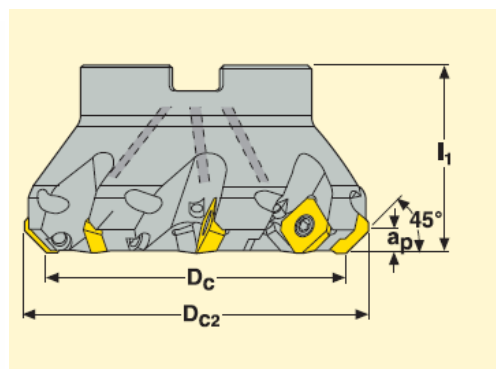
Фреза торцовая $\varnothing 20$ R217.53 – 0040-12-3А
